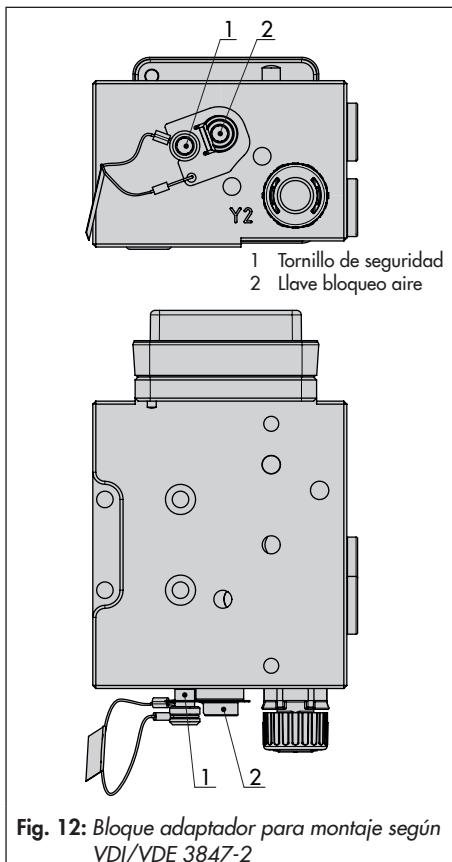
Bloque adaptador para montaje según VDI/VDE 3847-2
